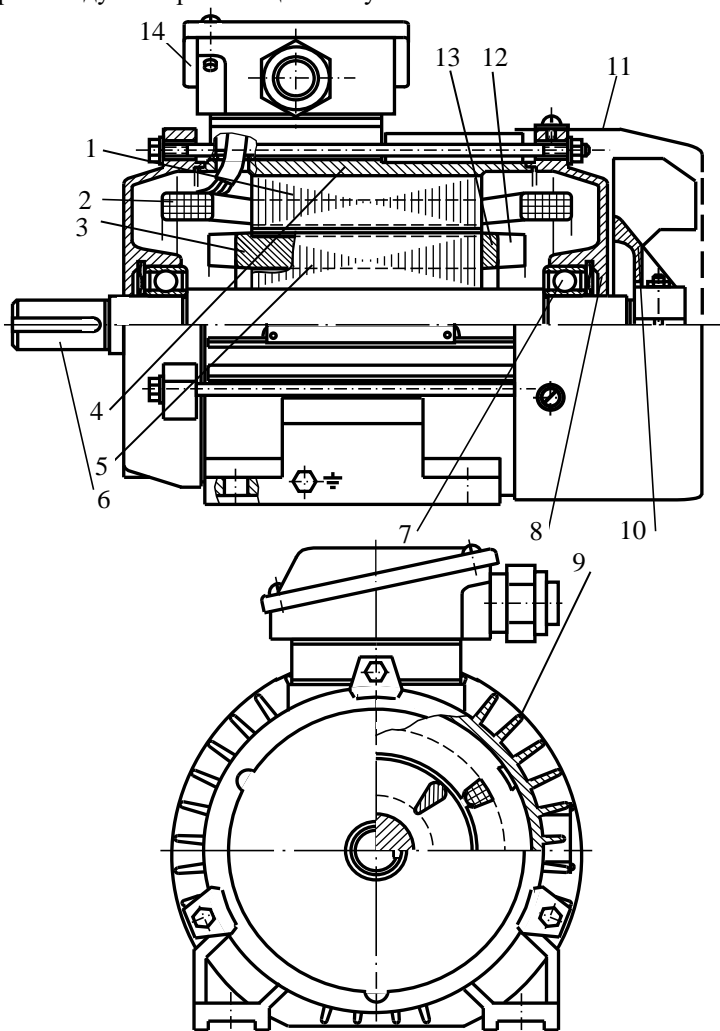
Асинхронный двигатель с короткозамкнутым ротором
